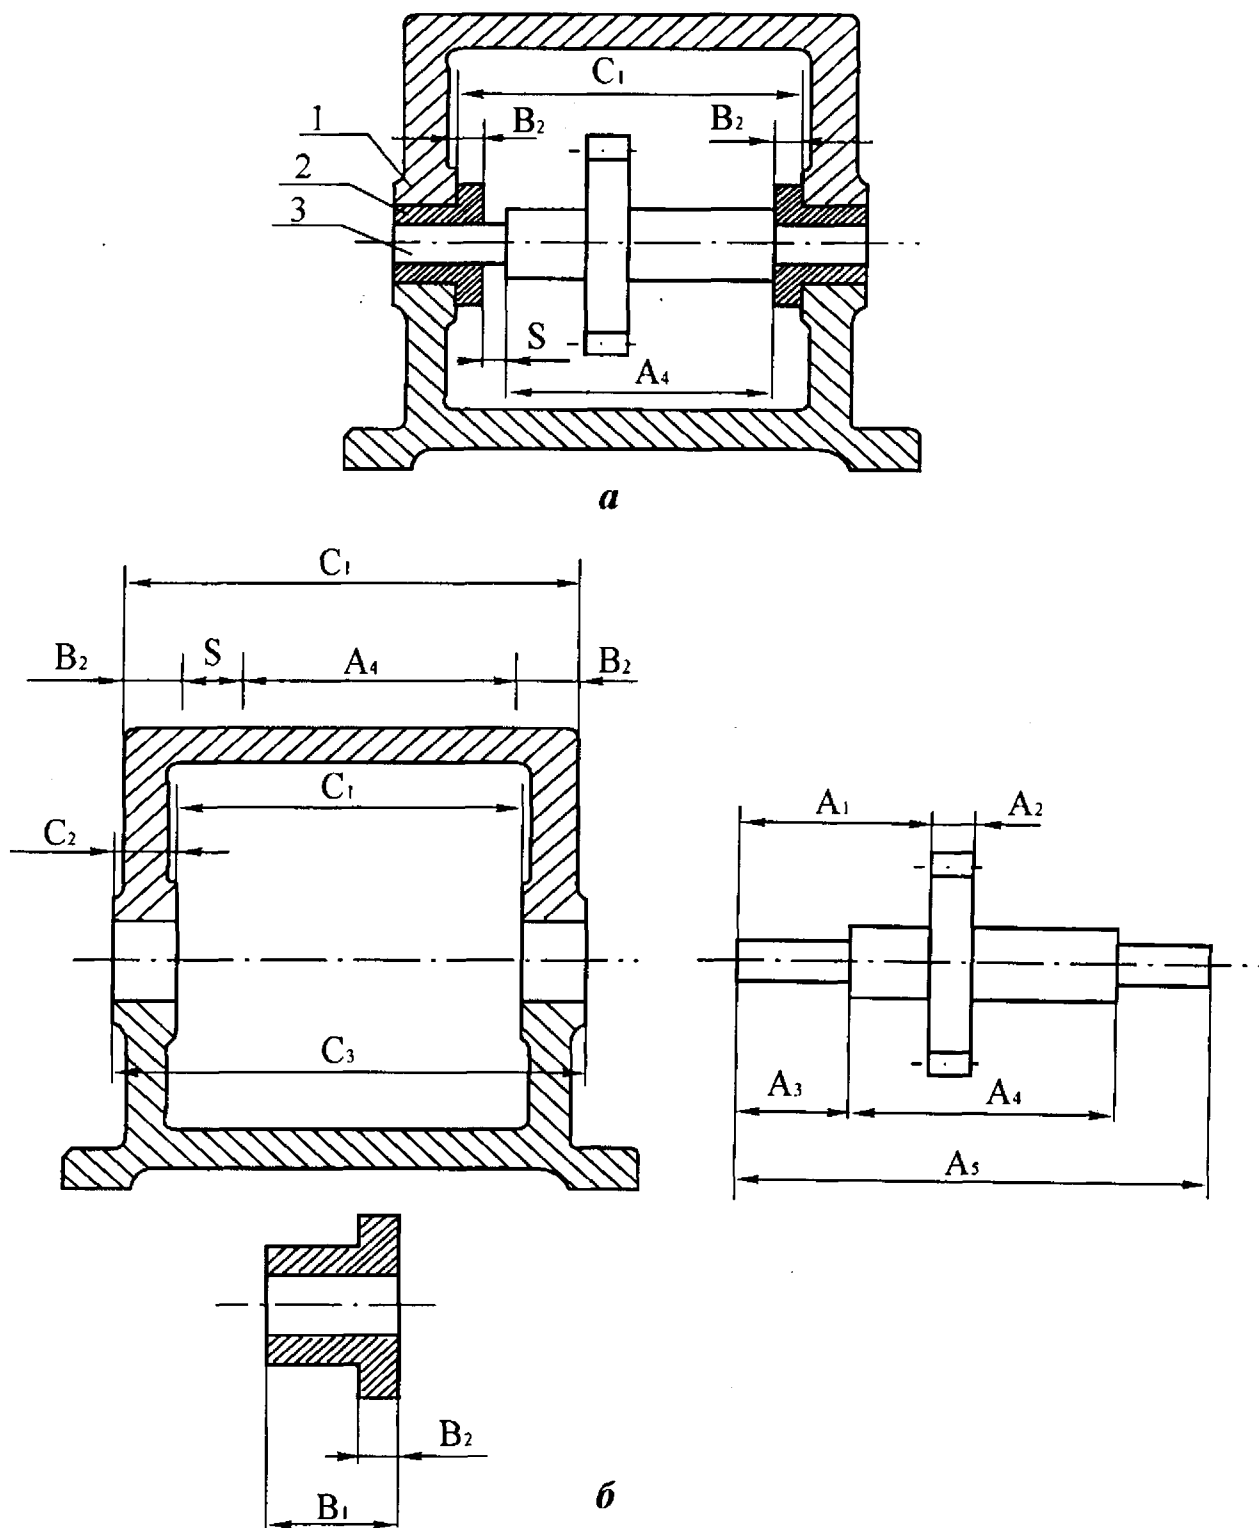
Разрез редуктора и чертеж деталей, входящих в узел
